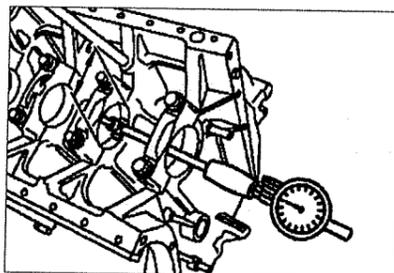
Измерение диаметров отверстий коренных подшипников.
